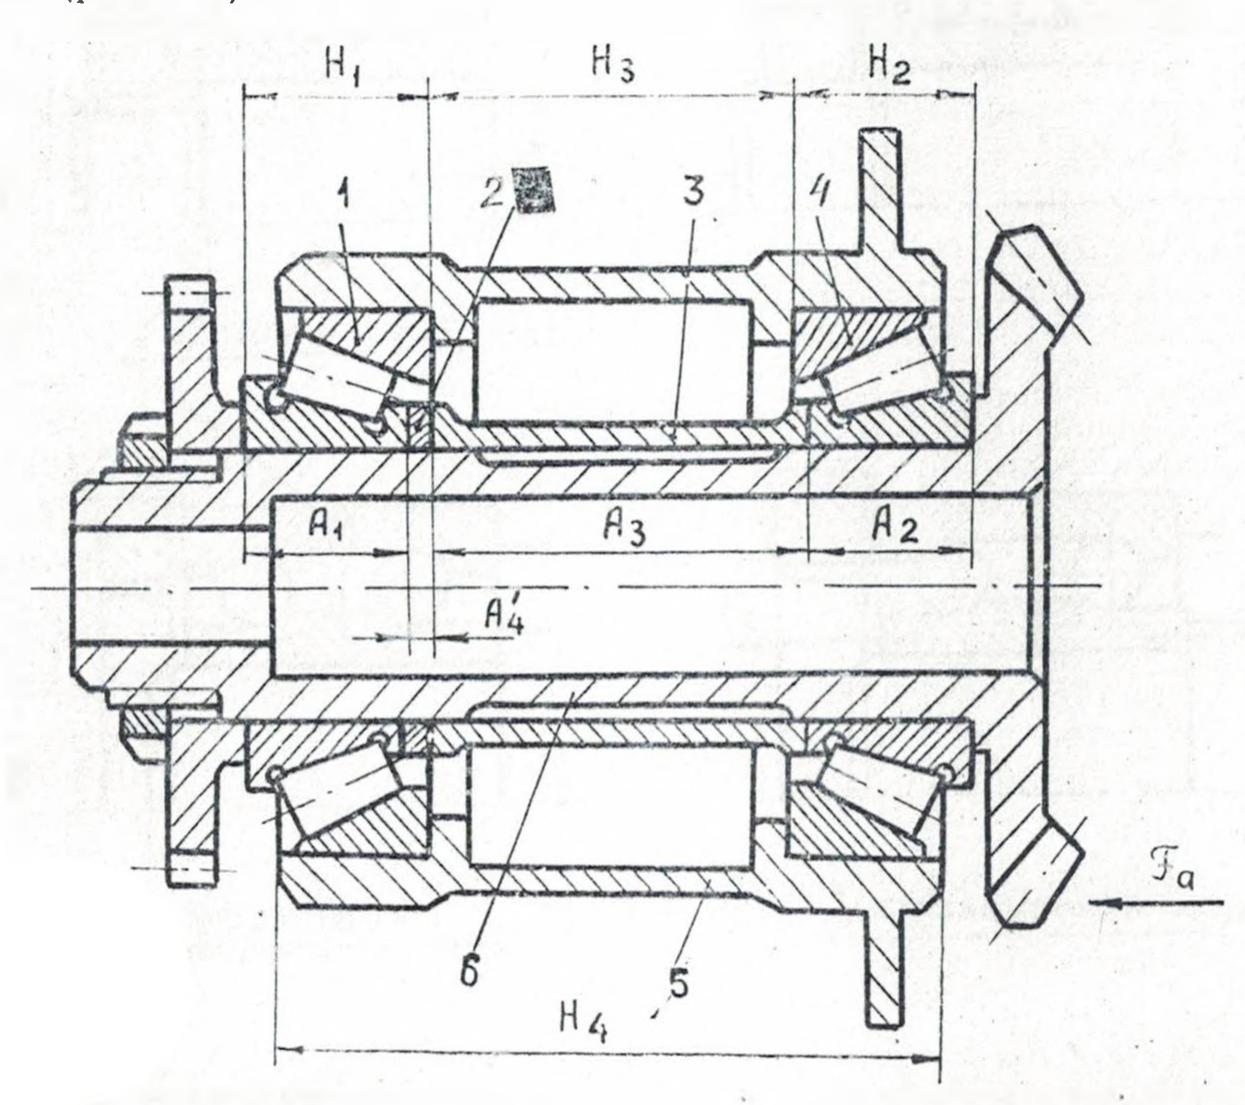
Подпишниковый узел редуктора: 1, 4 — роликовые подшипники; 2 — регулировочное кольцо; 3 — дистанционная втулка; 5 — корпус; 6 — вал-шестерня
